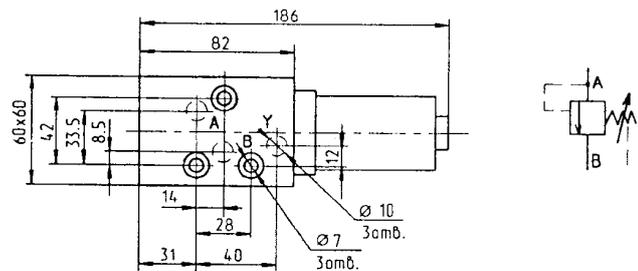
Гидроклапаны давления типа VB...-10K Hydraulik-Ring
